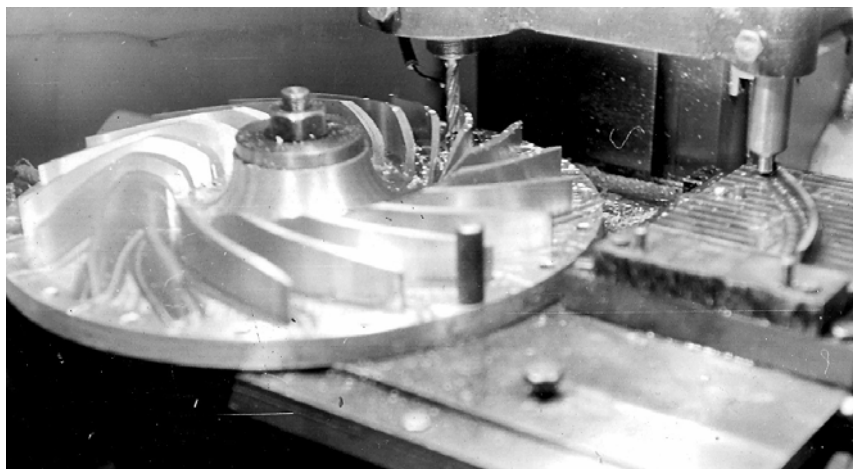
Обработка лопаток на поверхности основного диска РК на копировально-фрезерном станке (кафедра КВХТ СПбГПУ)
